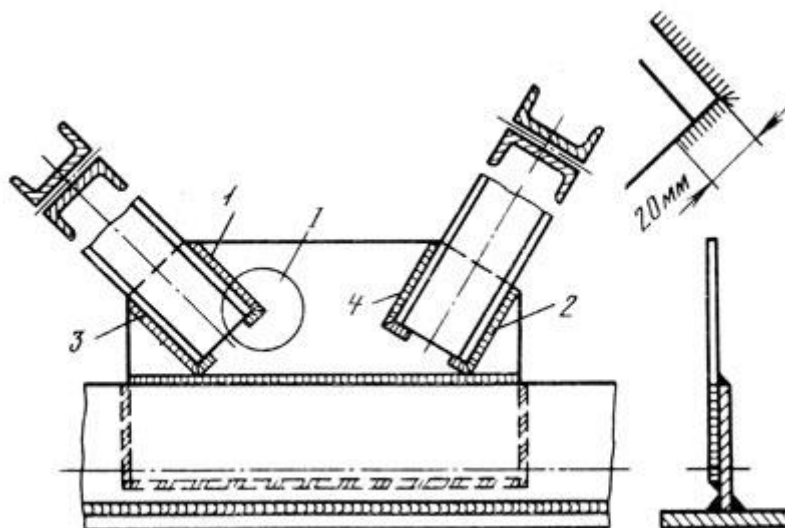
Порядок выполнения флангового (продольного) шва: 1 - 4 - последовательность сварки
